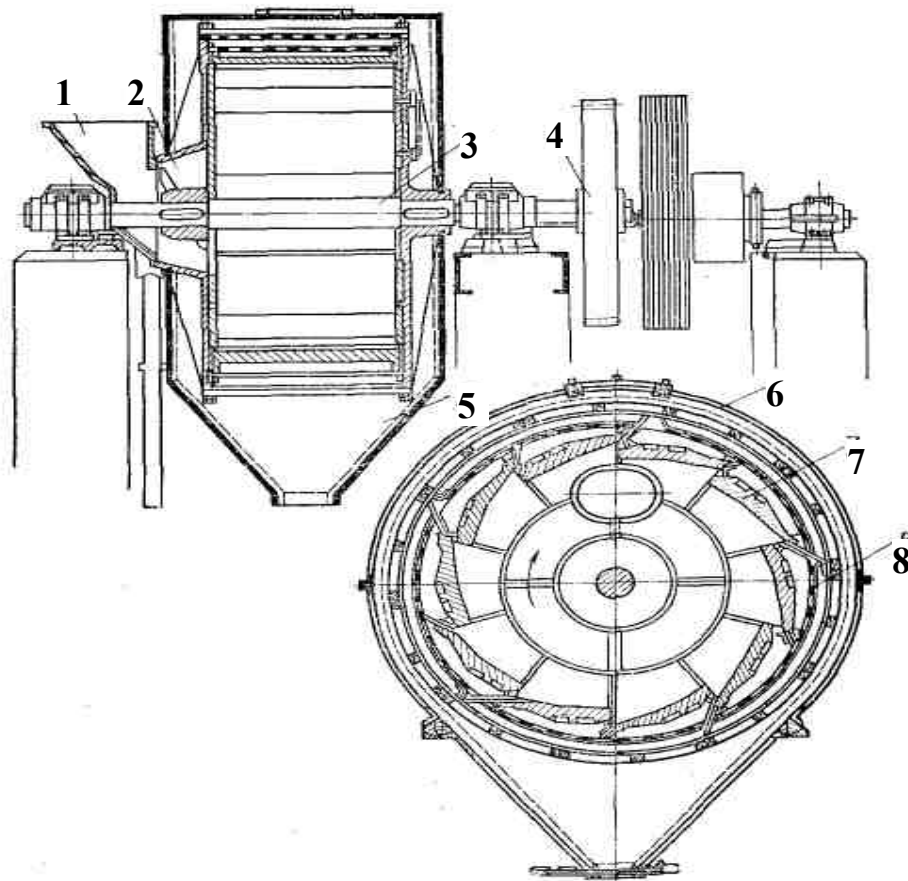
Кульовий млин безперервної дії: 1 – завантажувальний бункер; 2 – пустотіла цапфа; 3 – центральний вал; 4 – привід; 5 – розвантажувальний бункер; 6 – сталевий барабан; 7 – бронеплити; 8 – сита
